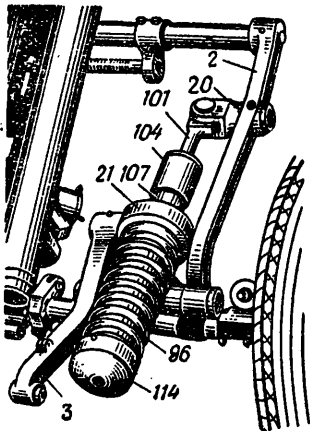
Общий вид уравновешивающего механизма, закрепленного на лафете:
